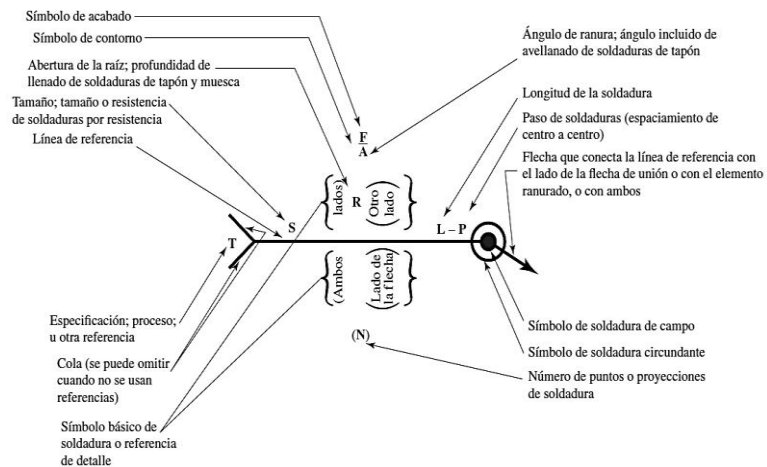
Representación simbólica de soldadura estándar AWS; (Helsel, 2010)
